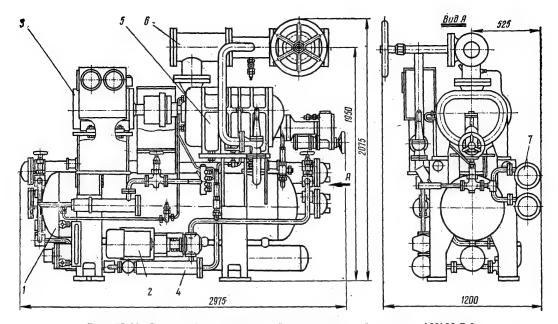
Винтовой поджимающий компрессорный агрегат АН130-7-6:
